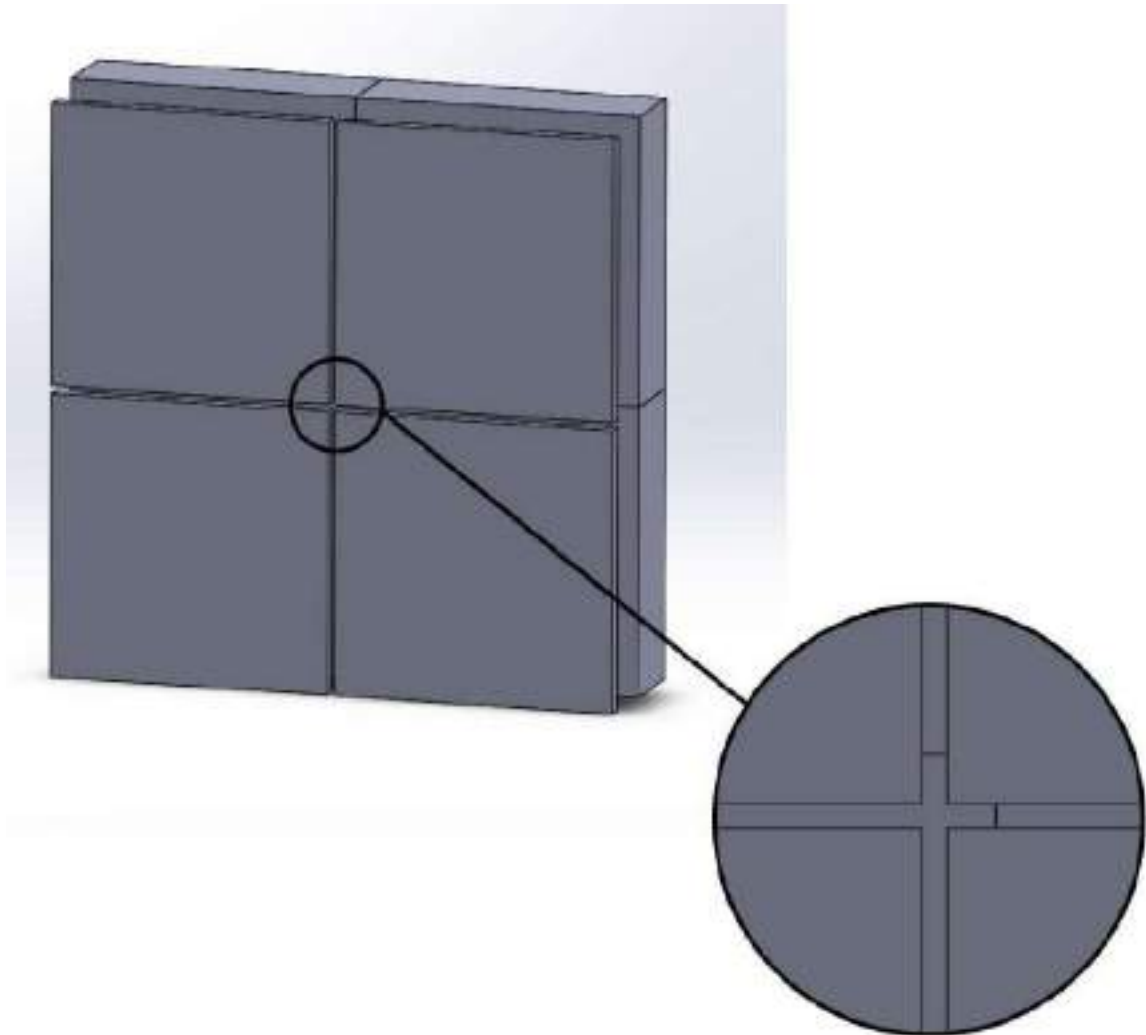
Sistema modular. Encaje de piezas, con detalle de unión.
